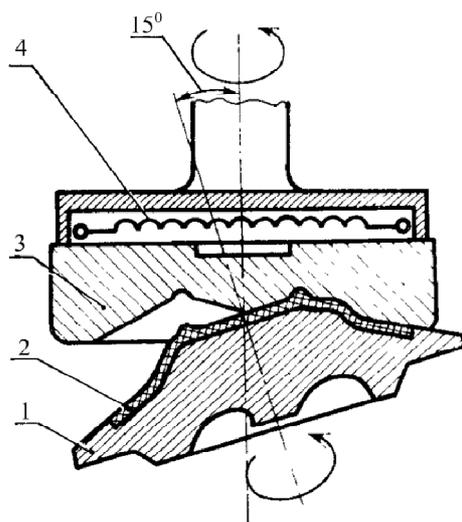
Схема формования плоских изделий роликовым шаблоном: 1 - гипсовая форма; 2 – масса; 3 – ролик; 4 – нагревательный элемент
